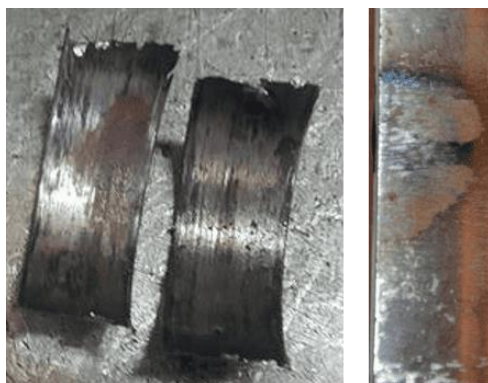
Bronzes gastos à esquerda), e gripados por *fretting* à direita).
